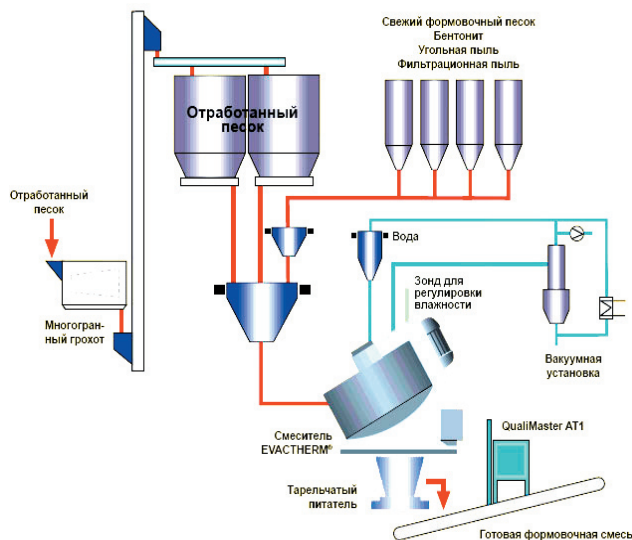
Процесс приготовления формовочной смеси в смесителе EVACTHERM® с вакуумным охлаждением [12]
